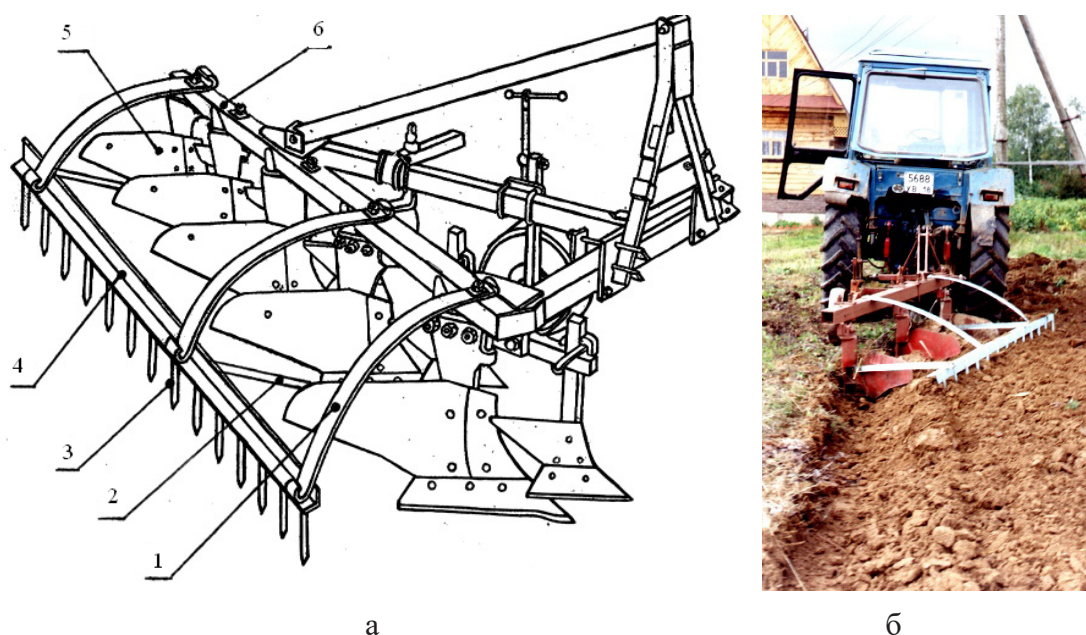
Комбинированный почвообрабатывающий агрегат:
